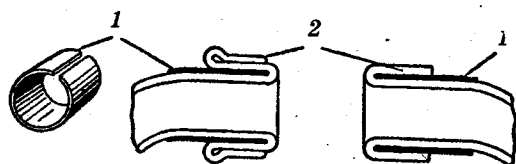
Стыковка камеры с помощью разрезных цилиндров:
